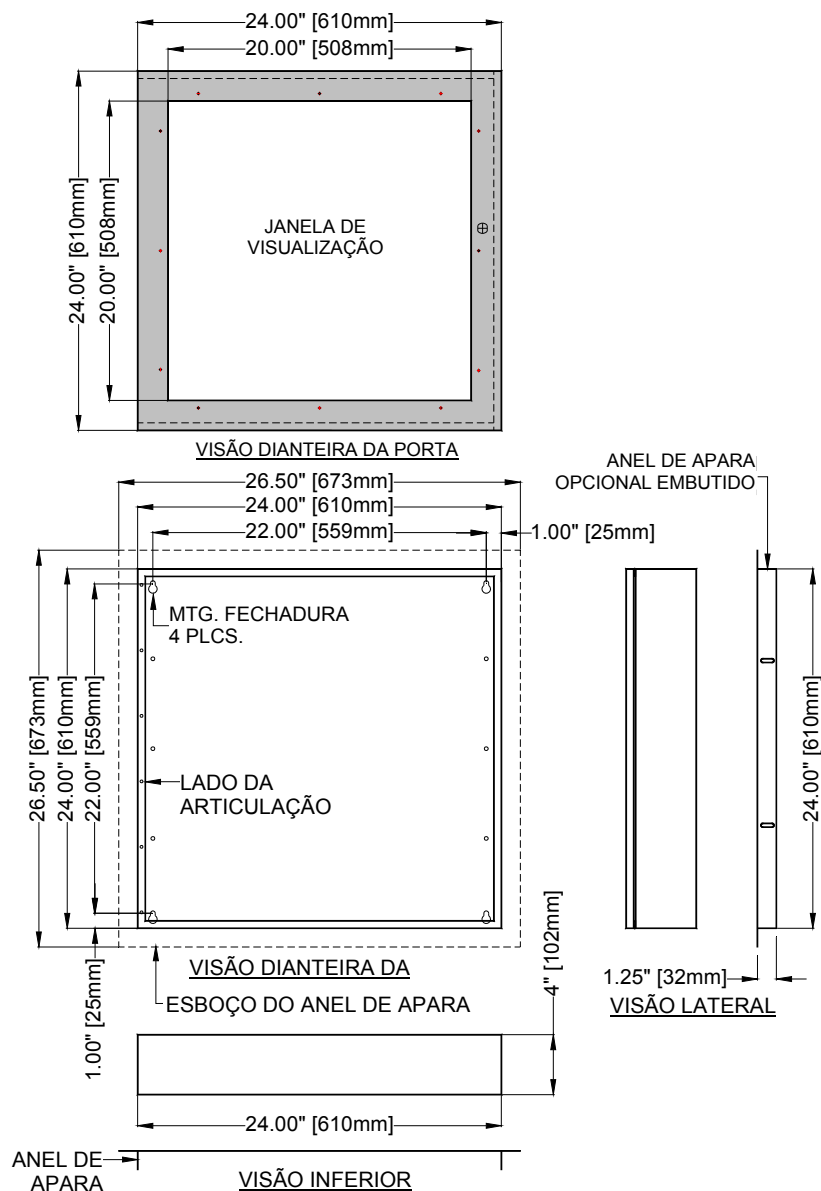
10-122 Dimensões do conjunto de portas e da back-box
